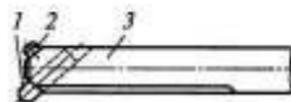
Расточный резец, применяемый на токарно-револьверных станках:
